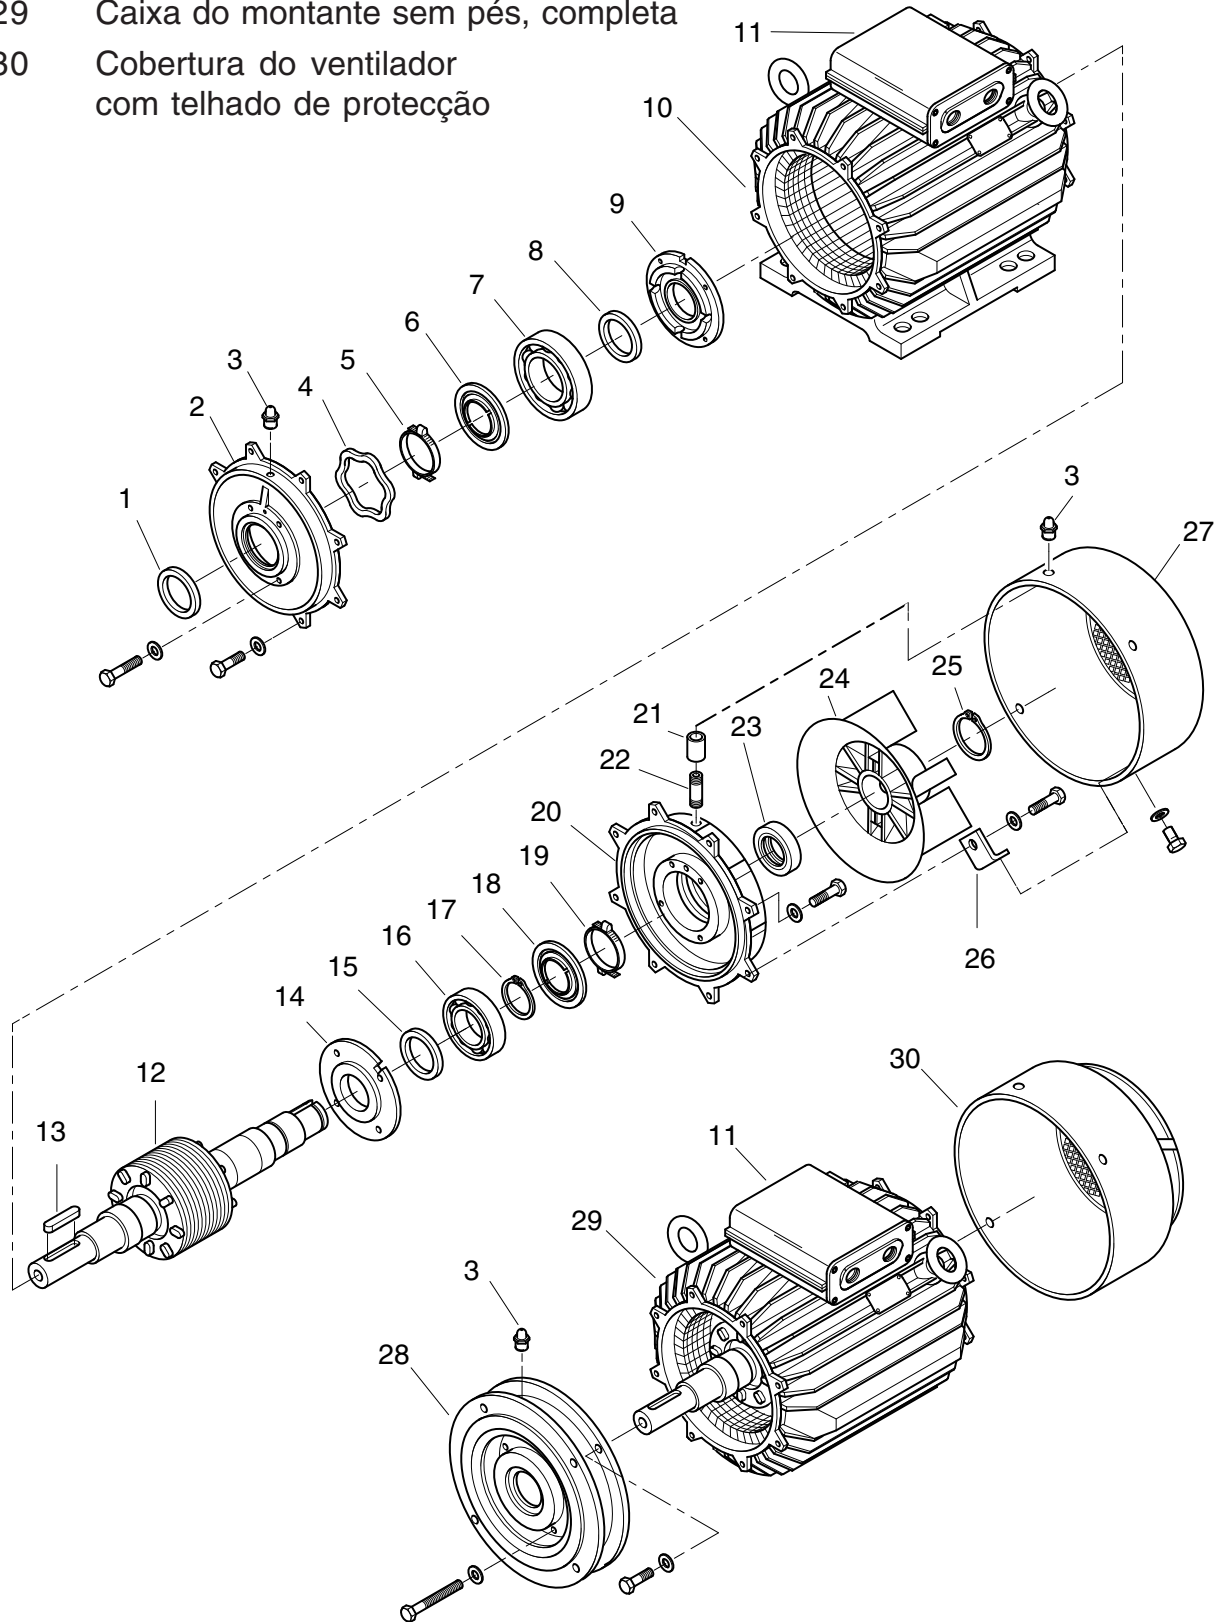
Vista explodida, IP55, Tamanho 180M-315L
